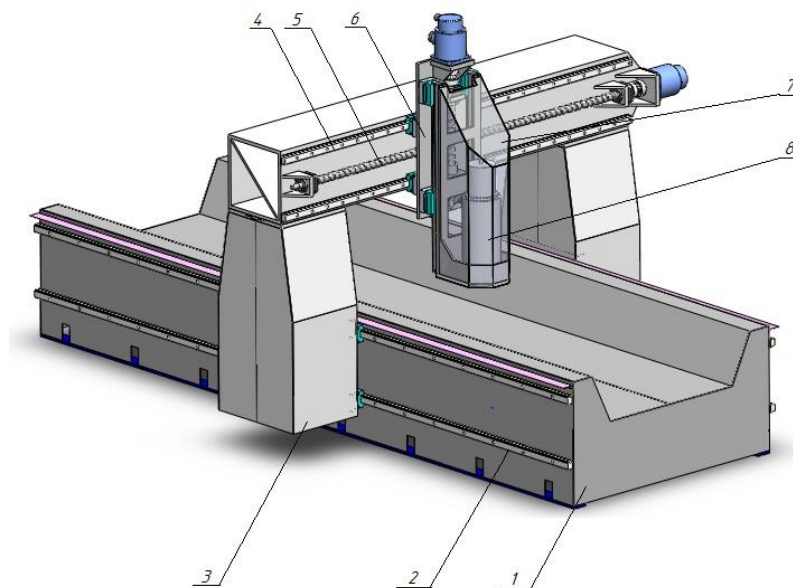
Модель деревообрабатывающего многоцелевого станка с ЧПУ
